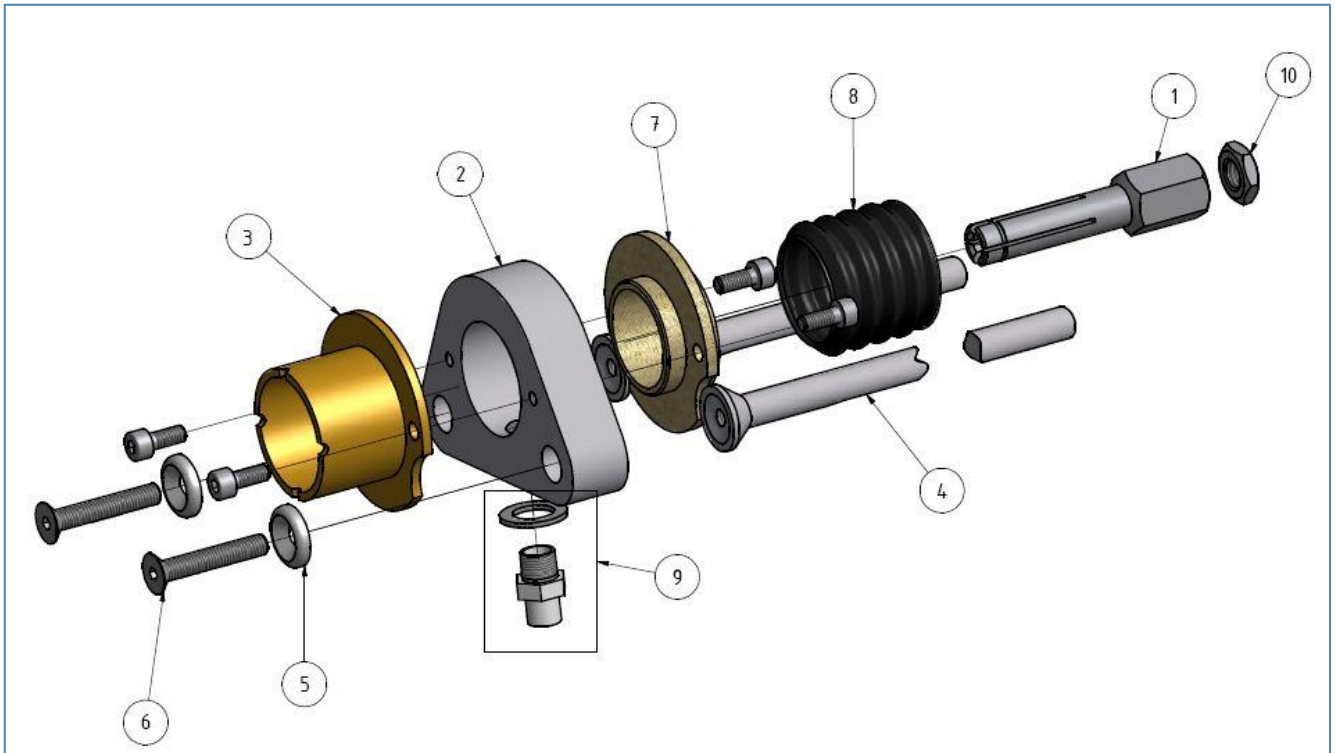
Stützeinrichtung für das Schutzgasbolzenschweißen
